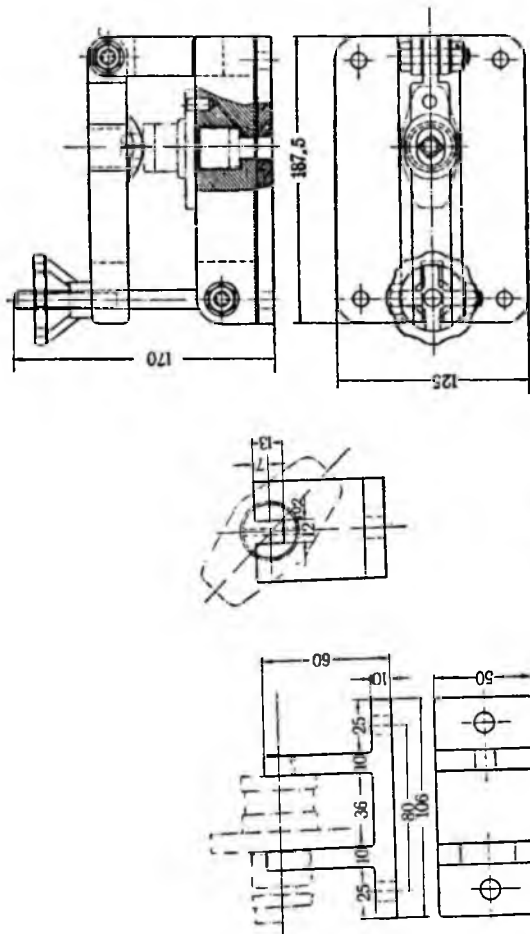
Приспособление для разборки и сборки механизма ручной подкачки насоса ЧТЗ.
